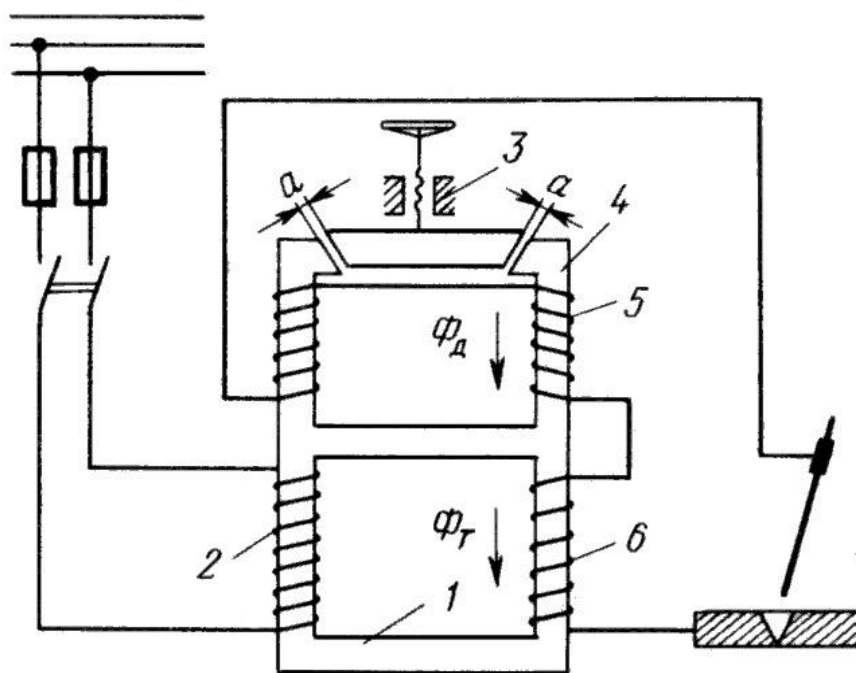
Схема сварочного аппарата со встроенным дросселем
